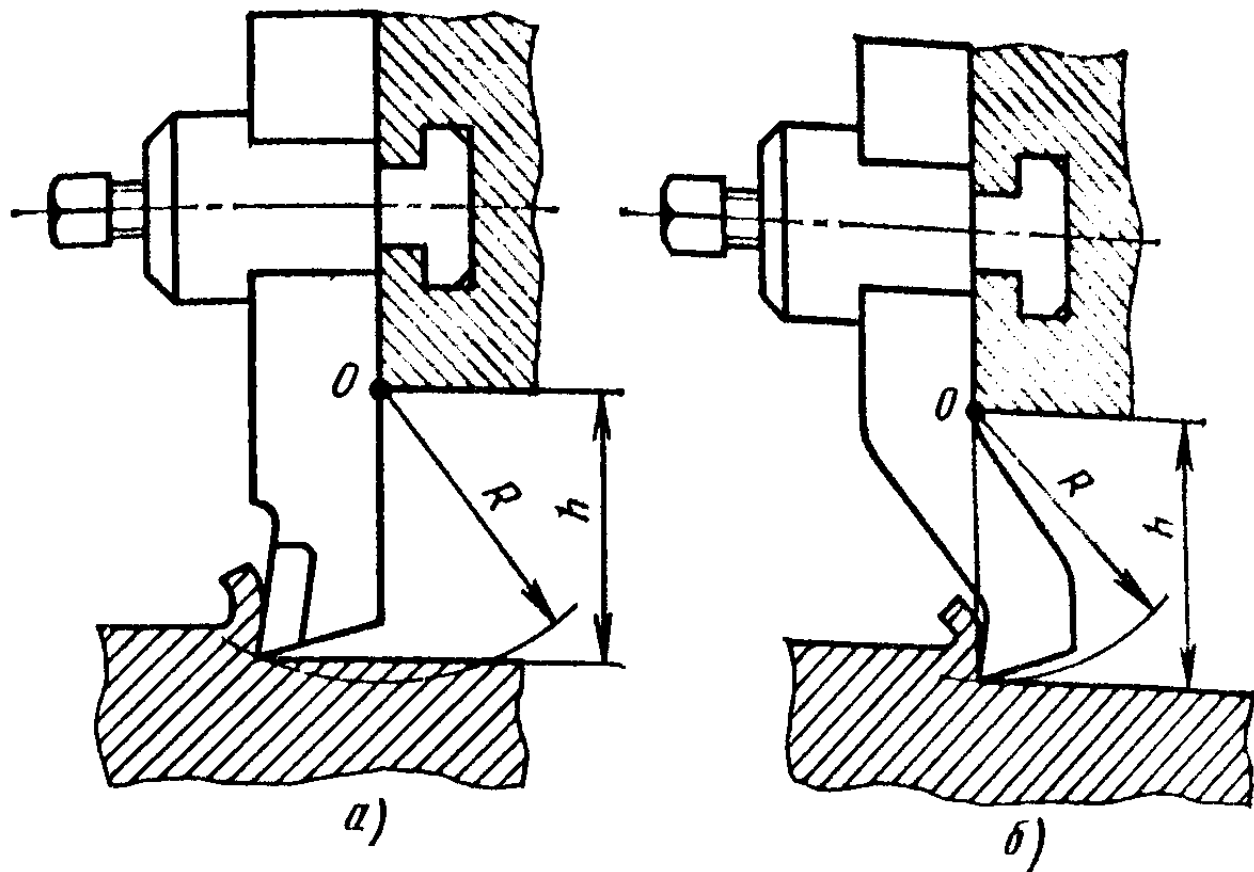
Конструктивные особенности строгальных резцов: а — стержень резца прямой; б — стержень резца изогнутый
